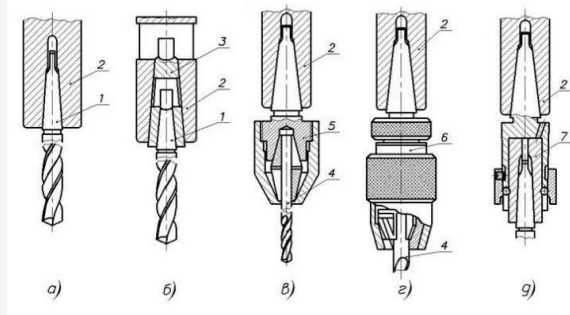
Способи установки інструменту на свердильному верстаті
